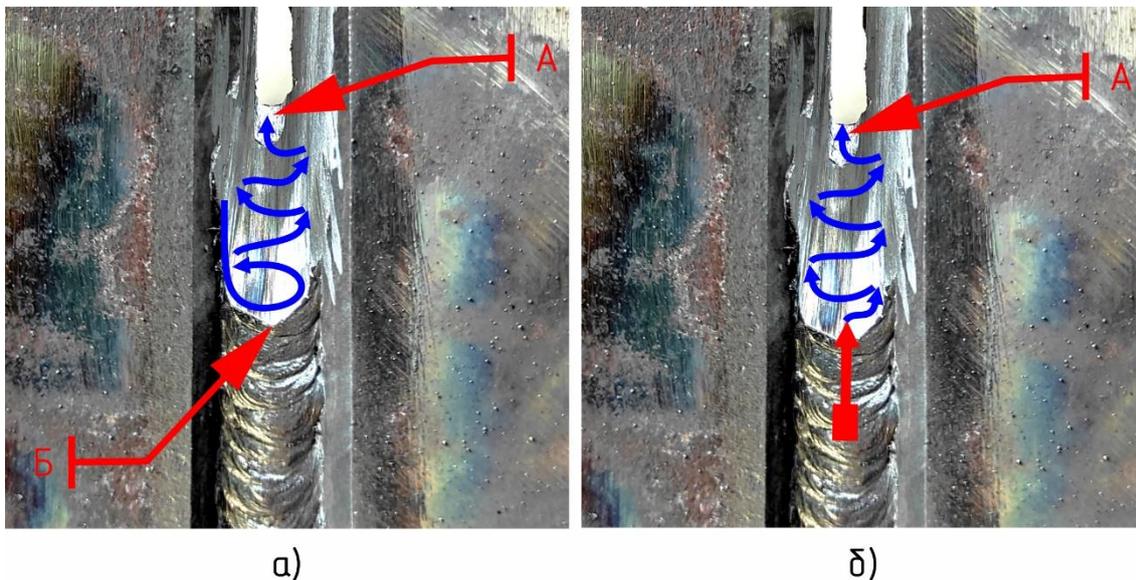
Техника возобновления корневого шва в вертикальном положении: а) при сварке в один проход; б) при сварке в несколько проходов.
